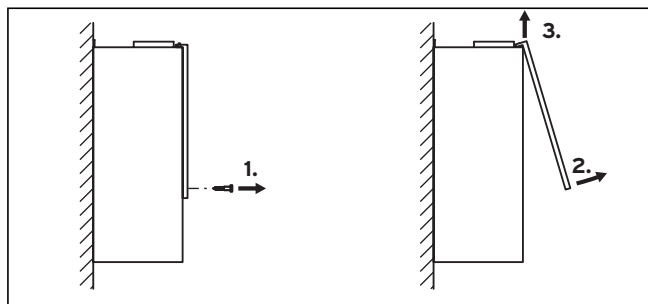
Démontage du panneau frontal (chambre de dépression)
